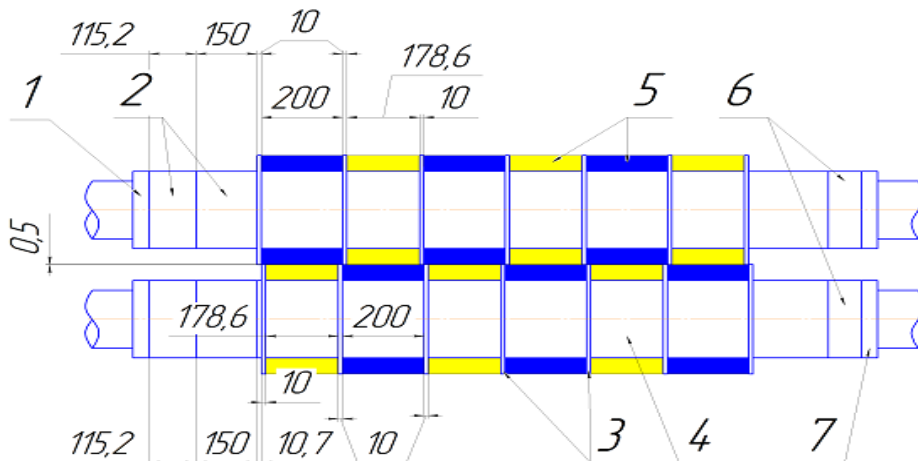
1 – упор вала; 2 – «корень»; 3 – дисковые ножи; 4 – юстировочные кольца; 5 – резиновые кольца; 6 – гидрогайка; 7 – упорная гайка
